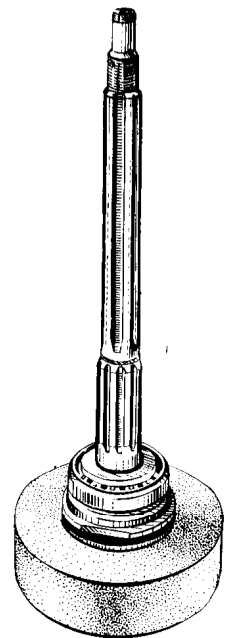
Спрессовка конического подшипника с ведущей шестерни главной передачи
